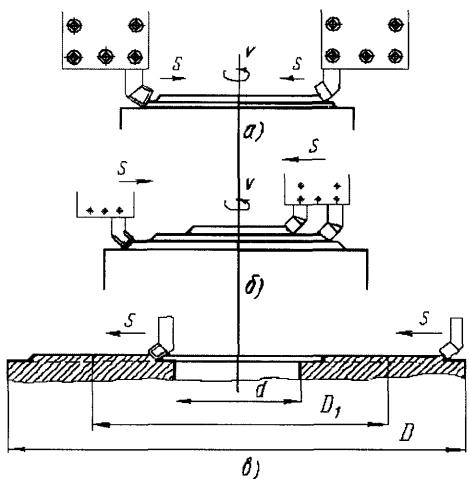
Схема обтачивания торцевых поверхностей двумя и тремя резцами с разделением припуска (а и б) и общей длины рабочего хода суппорта (в)
